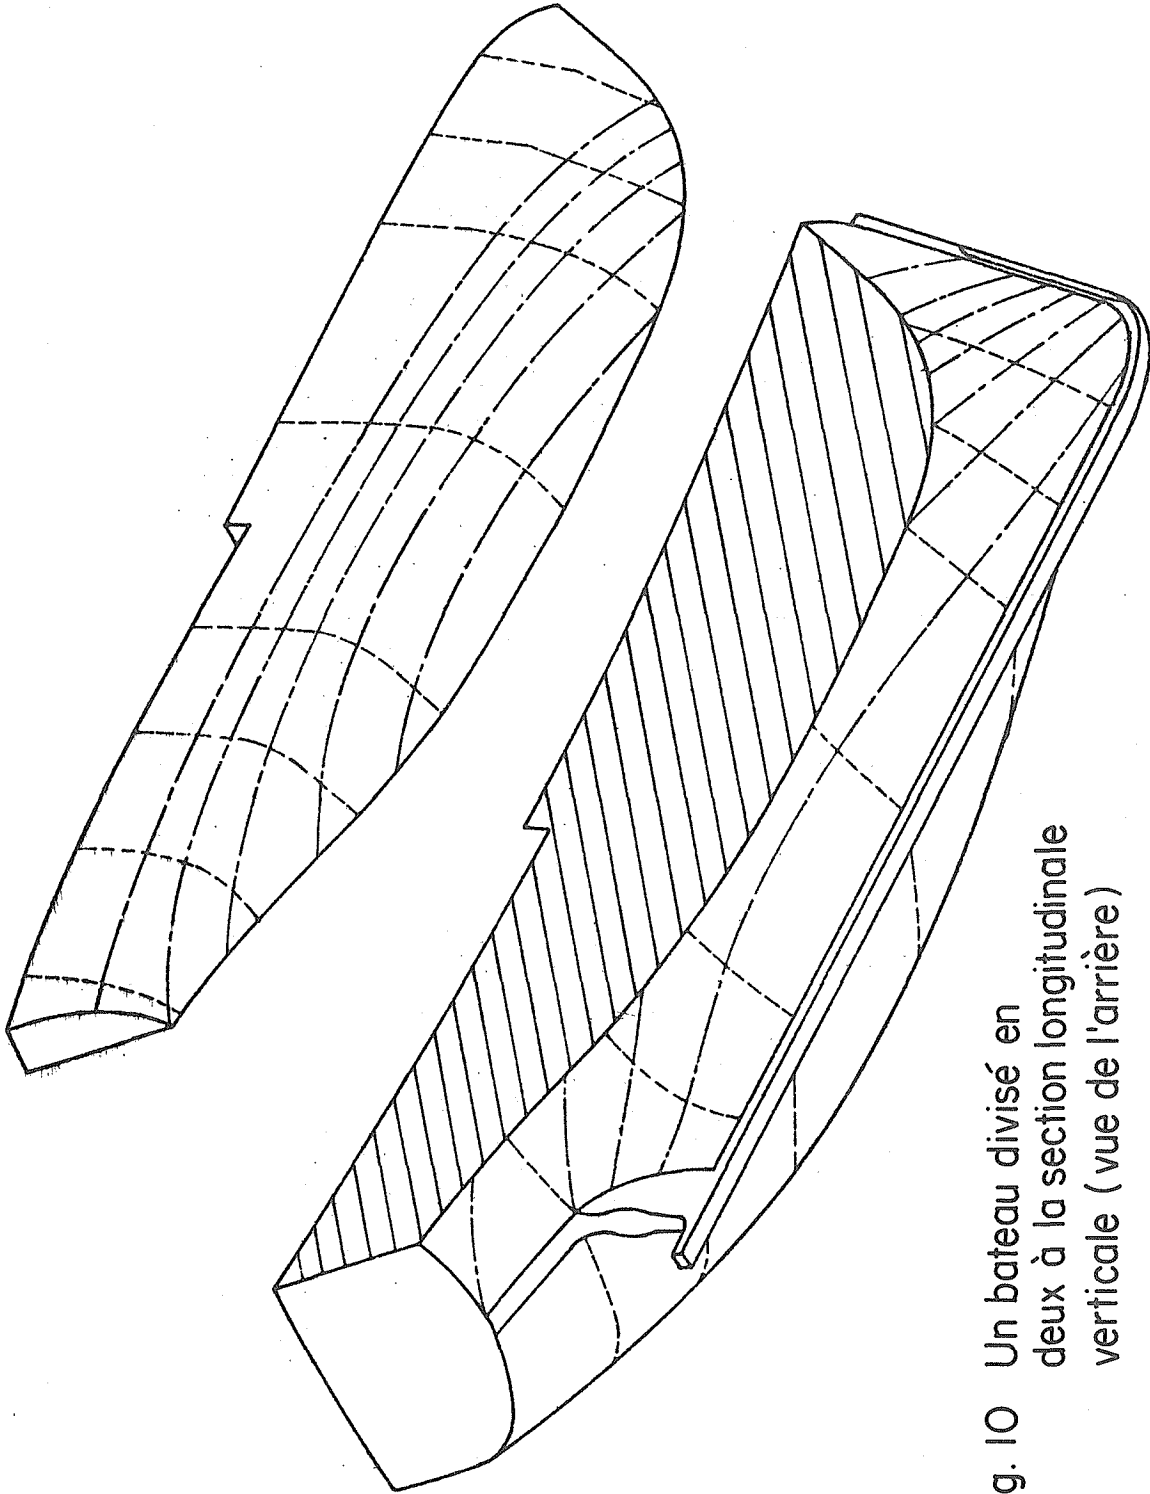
Un bateau divisé en deux à la section longitudinale verticale (vue de l'arrière)
